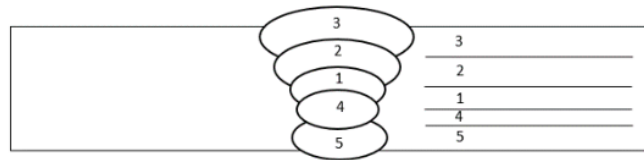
Perfil da seção transversal da solda após a soldagem, sequência de passes
